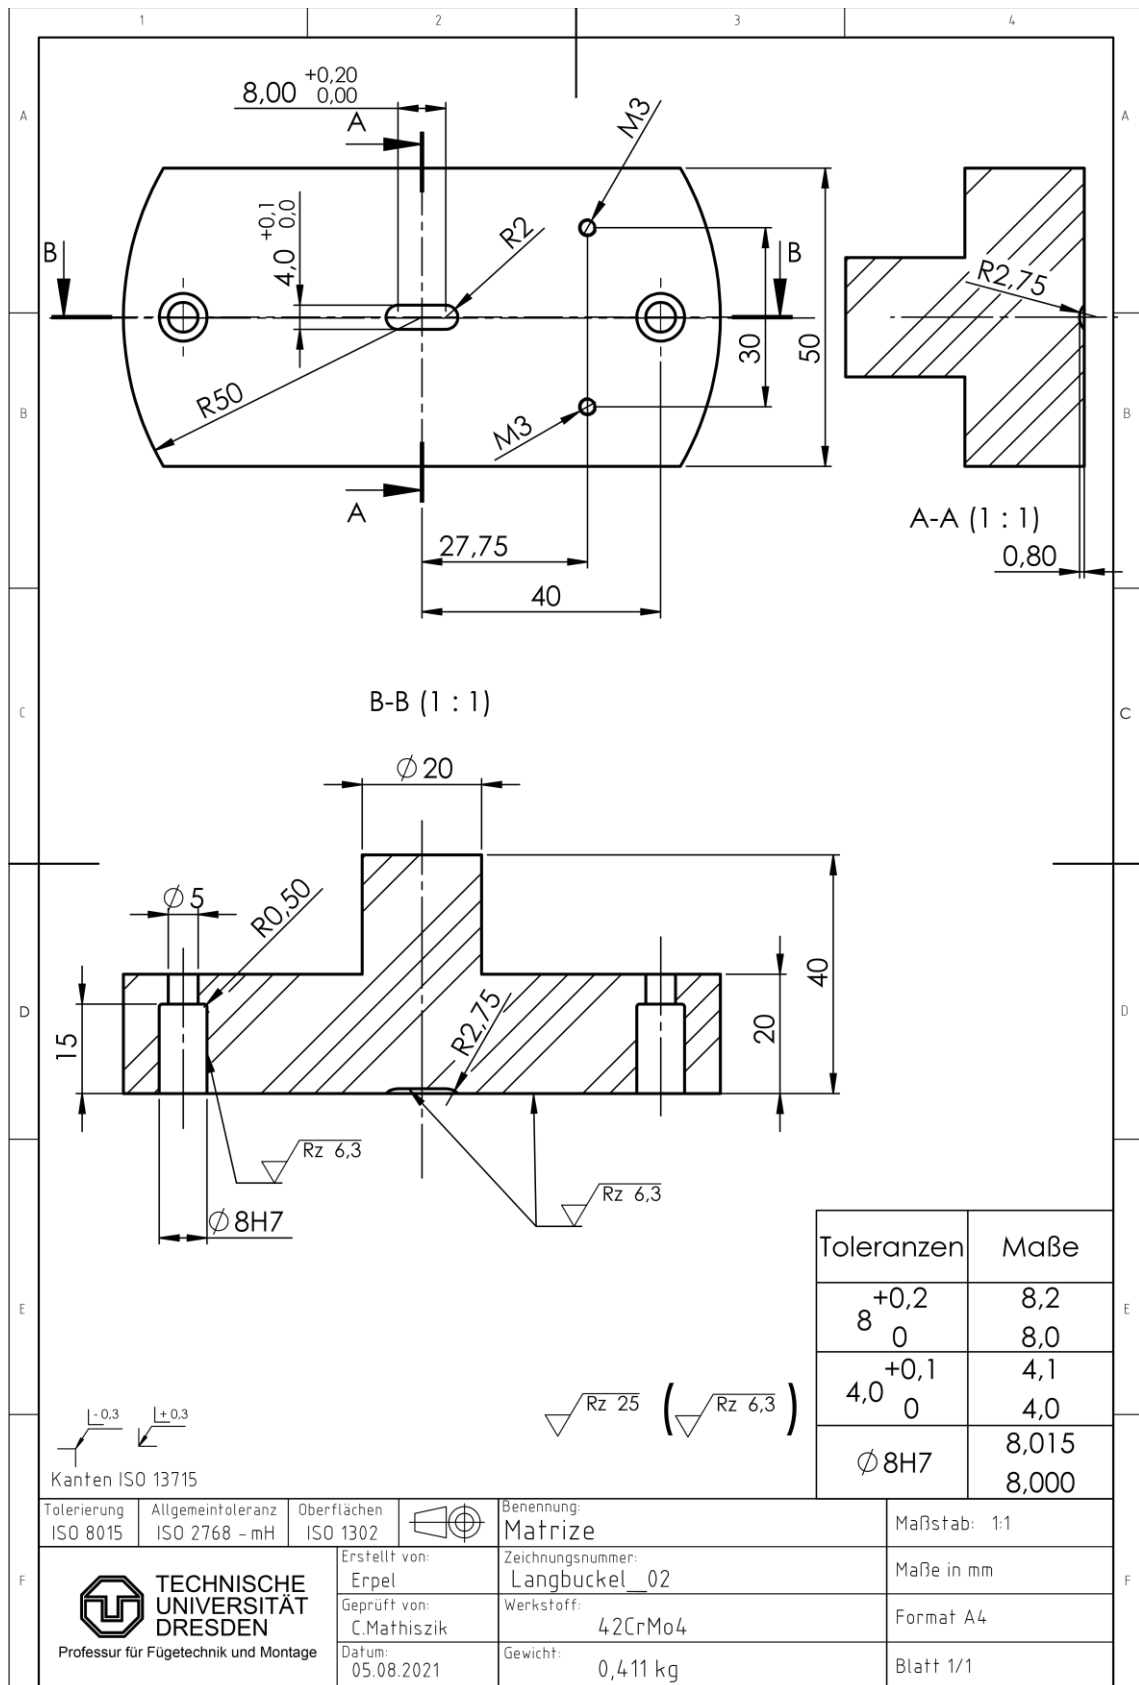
Technische Zeichnung des Matrizenwerkzeugs der Prägevorrichtung
